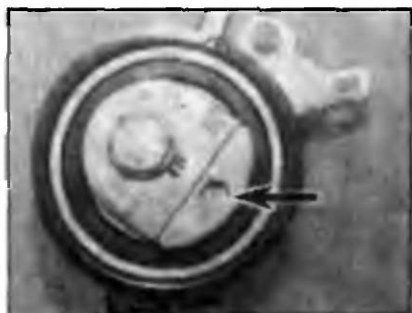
Отверстие для установки торцевого ключа на шкиве механизма натяжения и отвода шкива от ремня
